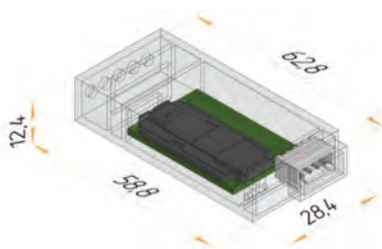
Внешний и внутренний вид корпуса модуля SCD30 с размерами
